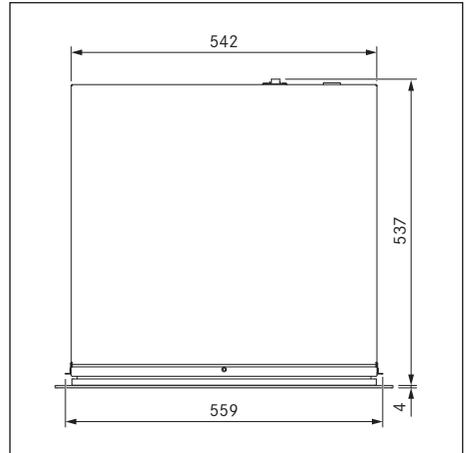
Dimensions MSS140 - Vue de dessus
